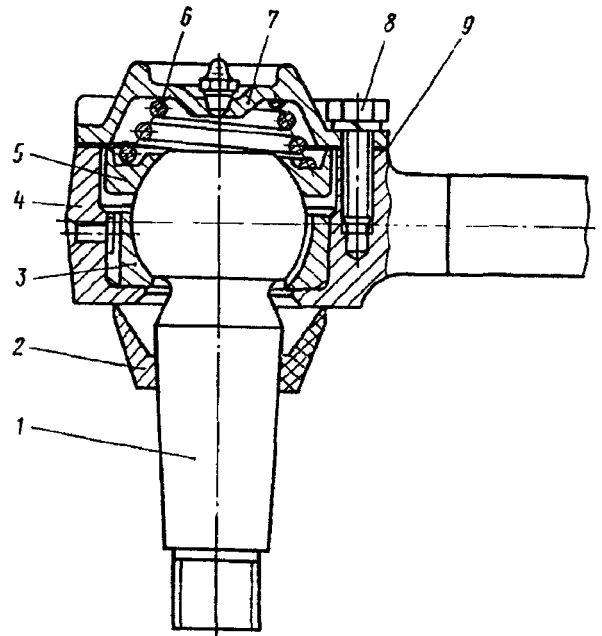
Головка реактивной штанги: 1 — палец шаровой; 2 — сальник; 3 — вкладыш внутренний; 4 — головка реактивной штанги; 5 — вкладыш наружный; 6 — пружина; 7 — крышка; 8 — болт; 9 — прокладка
